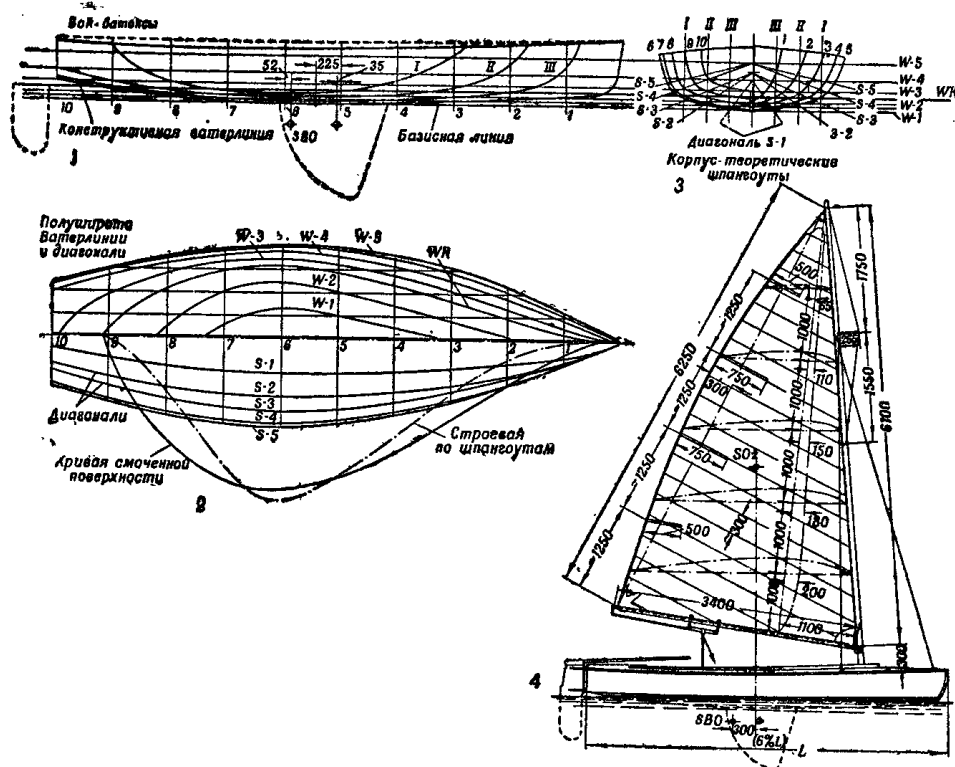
Теоретический чертеж яхты: 1 — бок, батоксы; 2 — полуширота, ватерлинии и диагонали; 3 — корпус, теоретические шпангоуты; 4 — план парусности
